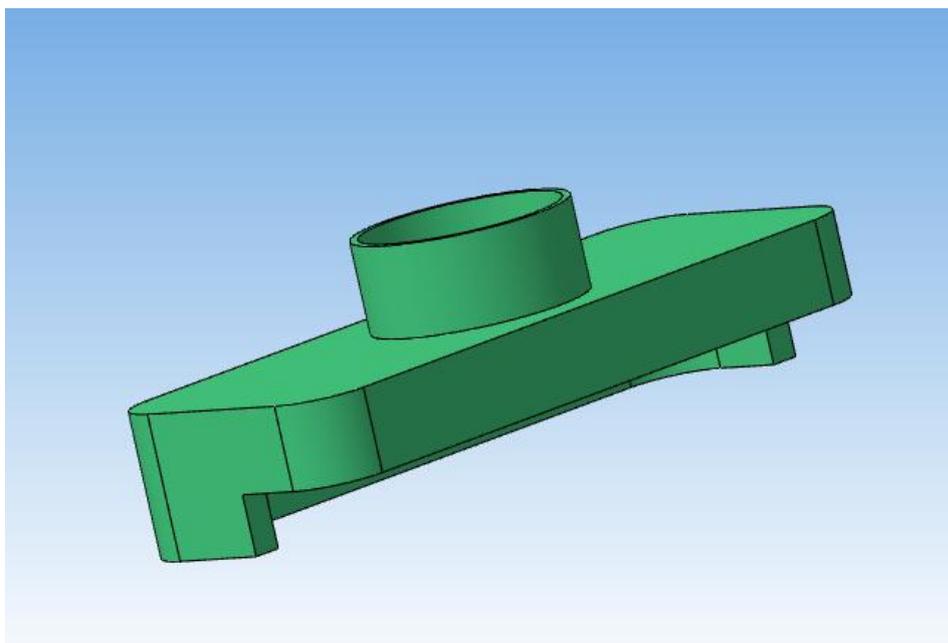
Внешний вид полимерного изделия «Деталь конструктора»
